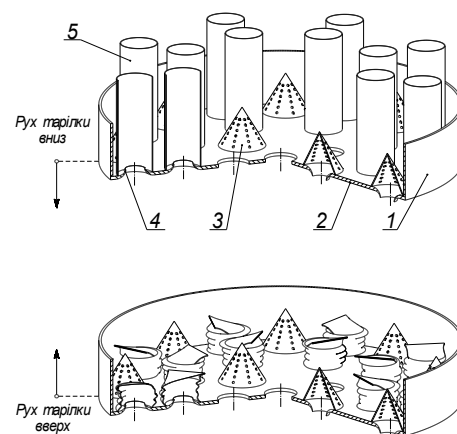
Вібротранспортувальний пристрій: 1 — борт; 2 — тарілка; 3 — фільтрувальний елемент; 4 — сопло; 5 — гнучкий патрубок
